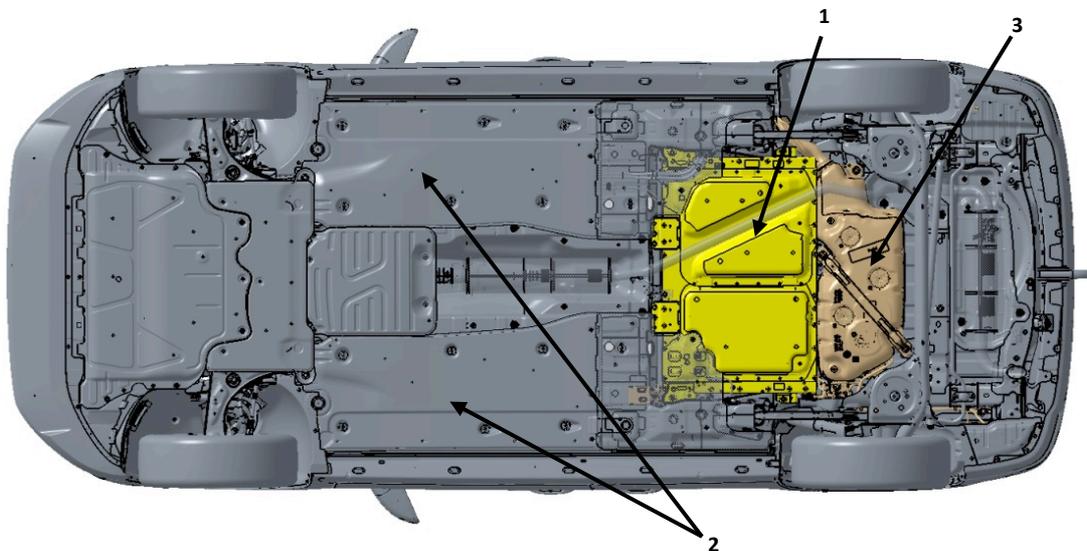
Vue de dessous position de la batterie haute tension, empattement court
